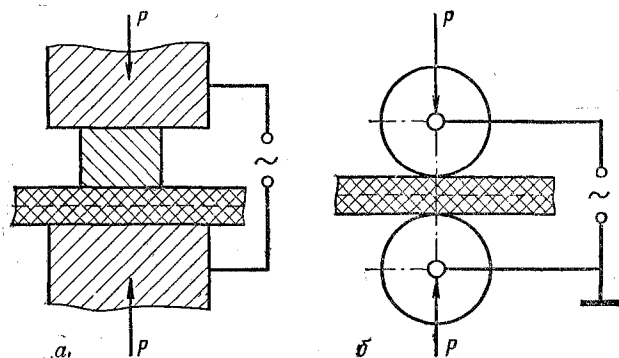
Схема прессового (а) и роликового (б) методов сварки токами высокой частоты
